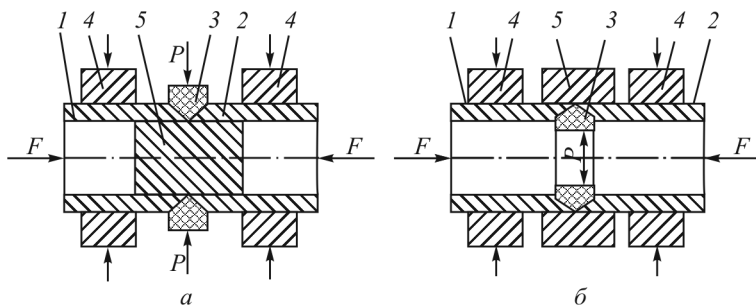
Схема радиальной СТ: а – с наружным разжимным кольцом; б – с внутренним разжимным кольцом; 1, 2 – свариваемые заготовки; 3 – вращающееся кольцо из присадочного материала; 4 – зажимные элементы; 5 – оправка
